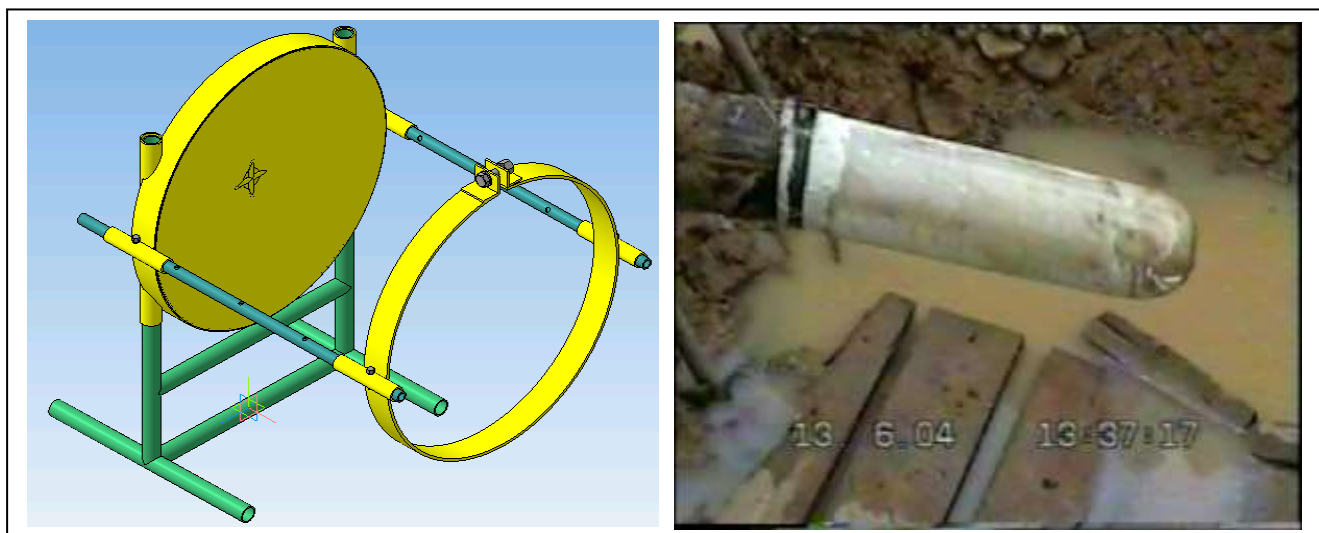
Устройство для изготовления комбинированного рукава
